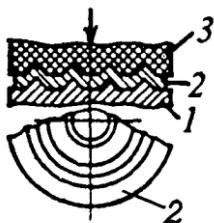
Схема формовки: 1 – матрица; 2 – изделие;
